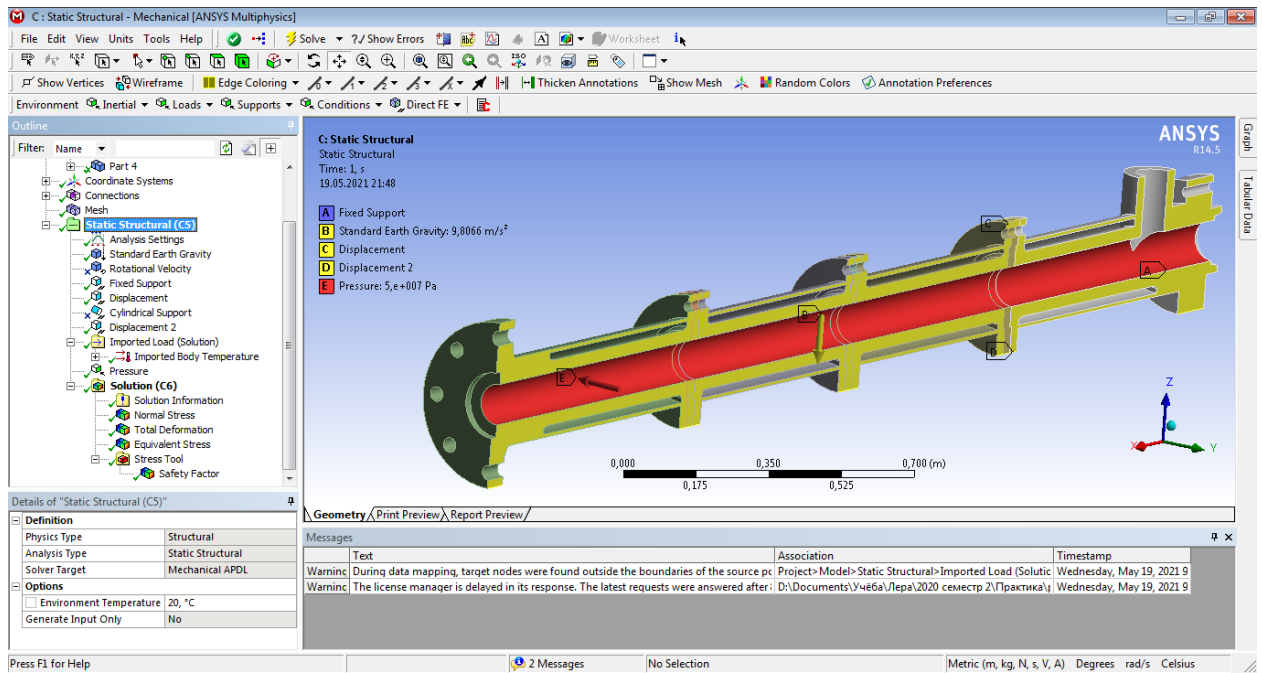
Розташування зусиль і опор для деталей корпусу
